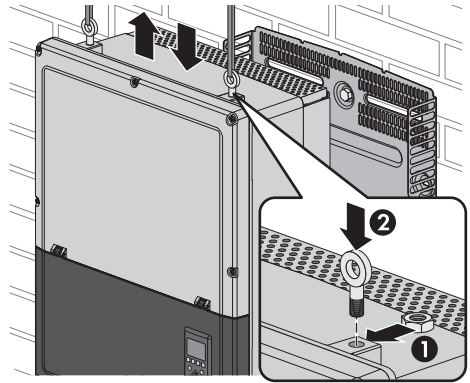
Augenschrauben befestigen und Wechselrichter anheben
